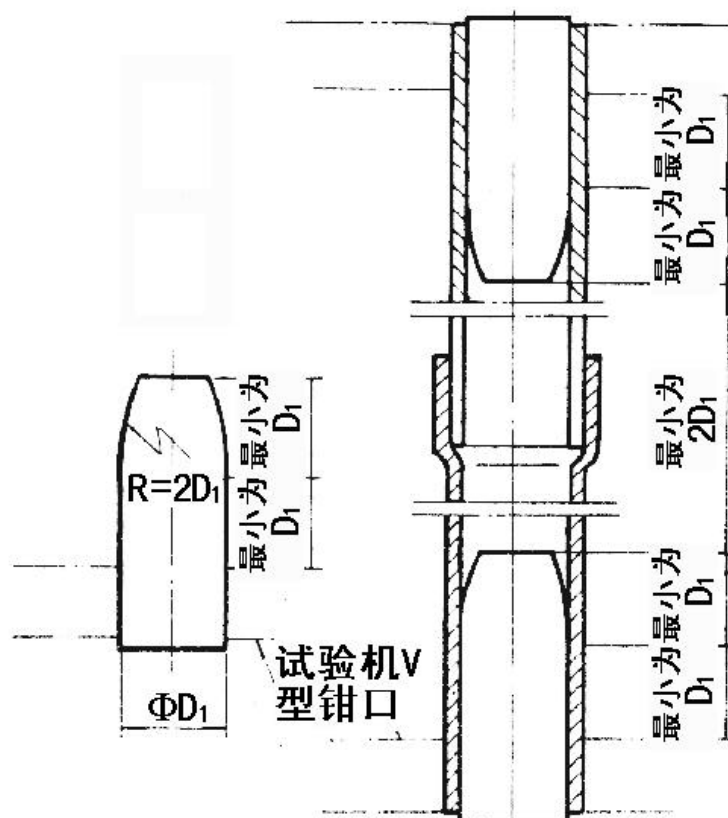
直径 76mm 管状钎焊接头拉伸试样
